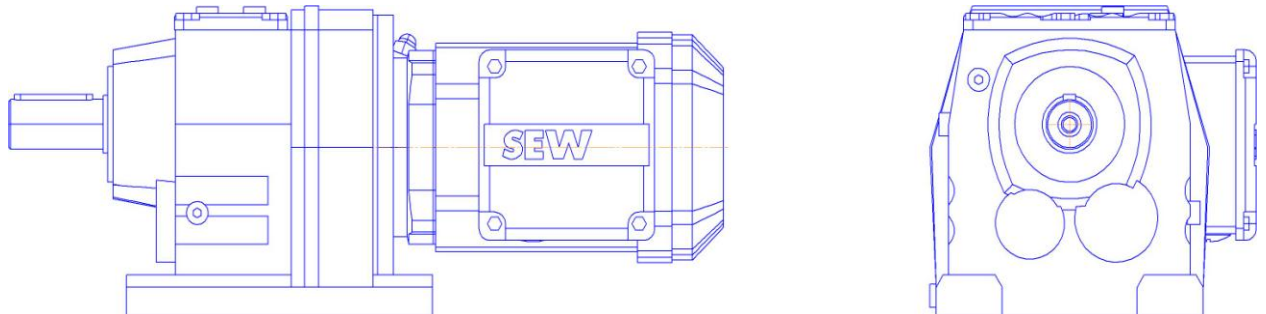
Загальний вид - мотор-редуктор SEW-EURODRIVE_ R47DRS71M4
